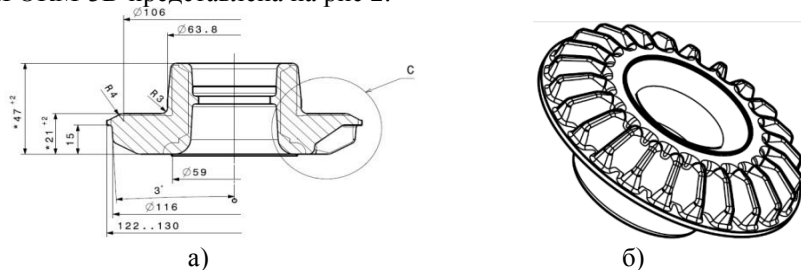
Чертеж (а) и твердотельная модель (б) детали конического зубчатого колеса
